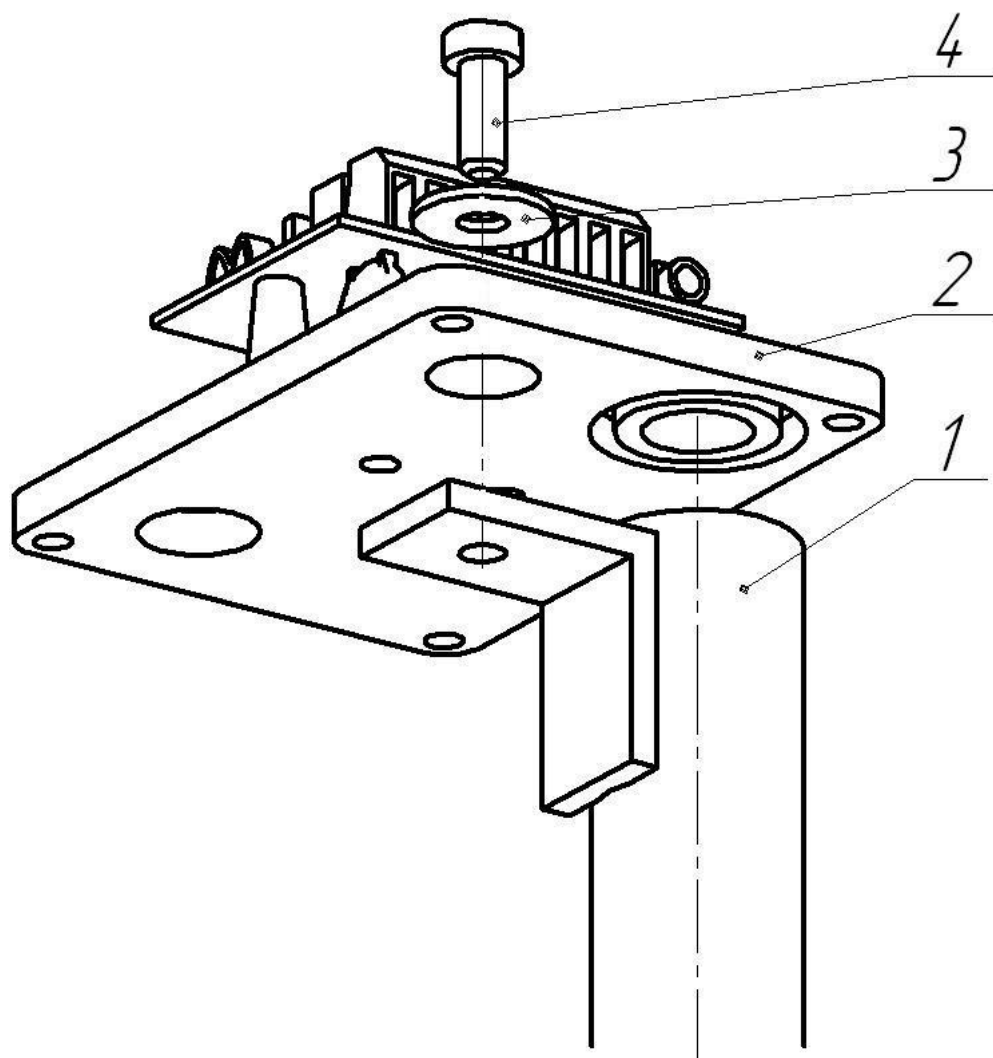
Крепление КМЧ-2 и КР-У1 на бетонное (кирпичное) ограждении
